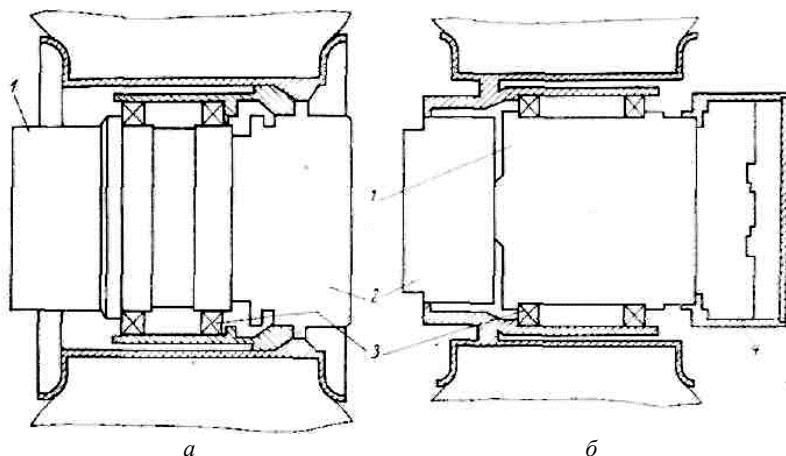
Схема мотор-колеса при компоновке IV вида:
